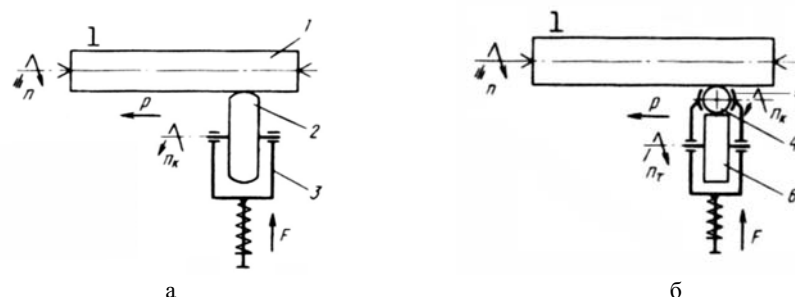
Схеми основних способів силової поверхневої обробки циліндричних деталей інструментального призначення із пружним притиском: а – дисками; б – кульками
